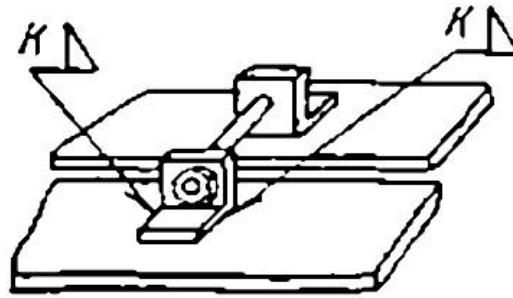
Стяжка с болтом и приваренными угольниками для сварки крупных конструкций из листового проката
